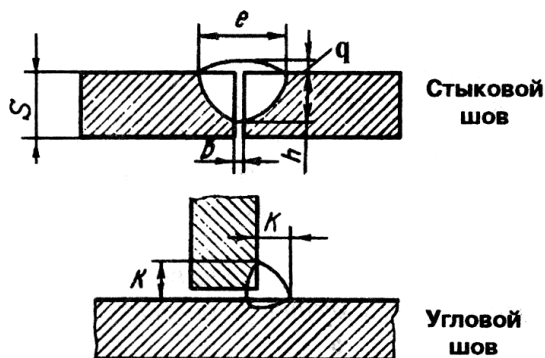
Основные конструктивные элементы сварных швов
